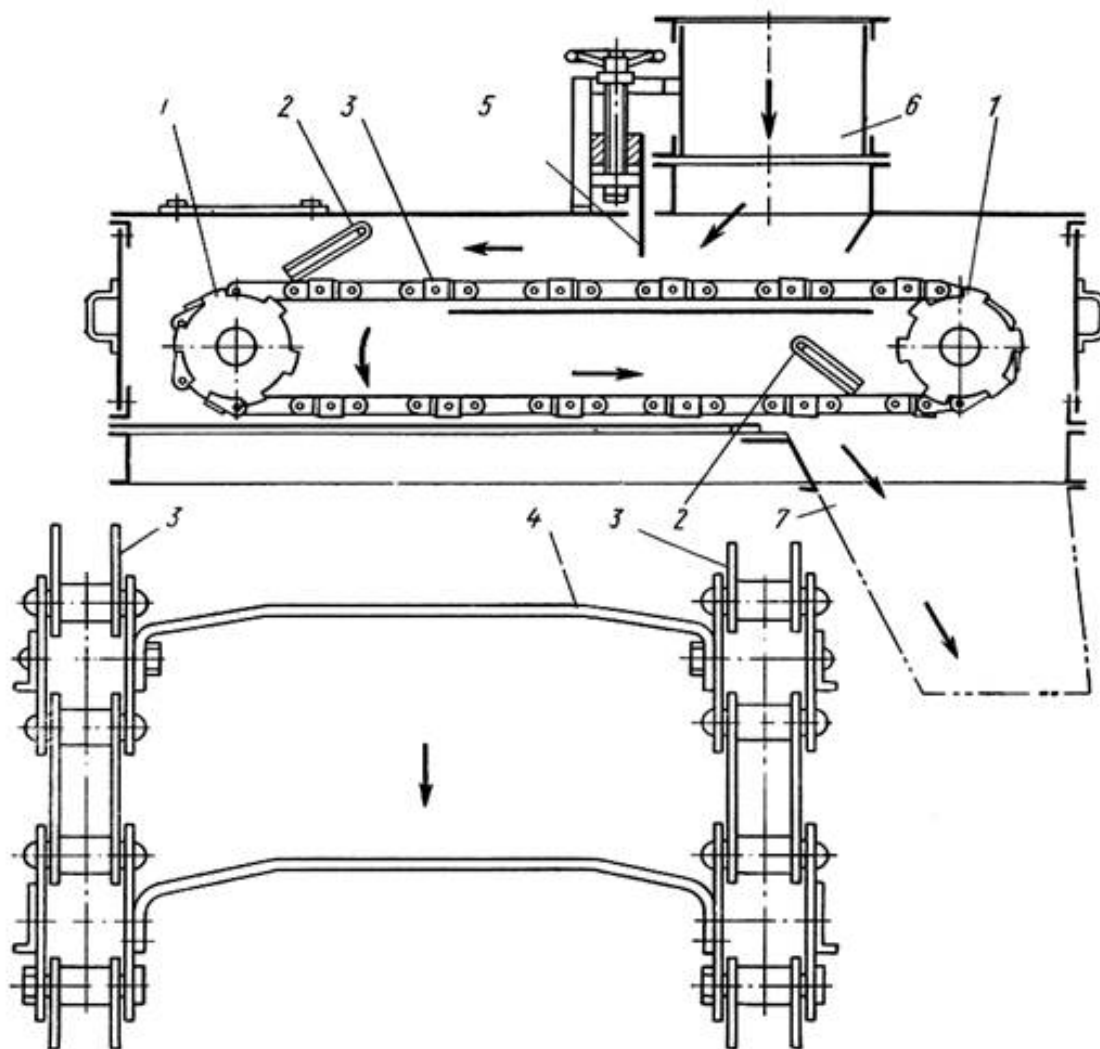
Скребок питатель сырого угля (внизу показан вид сверху на участок цепи): 1 – звездочка, приводящая в движение цепь, 2 – ограничитель, 3 – цепь, 4 – скребок, 5 – нож, регулирующий подачу топлива, 6 – приемный патрубок, подающий топливо в мельницу, 7 – патрубок, подающий топливо в мельницу
